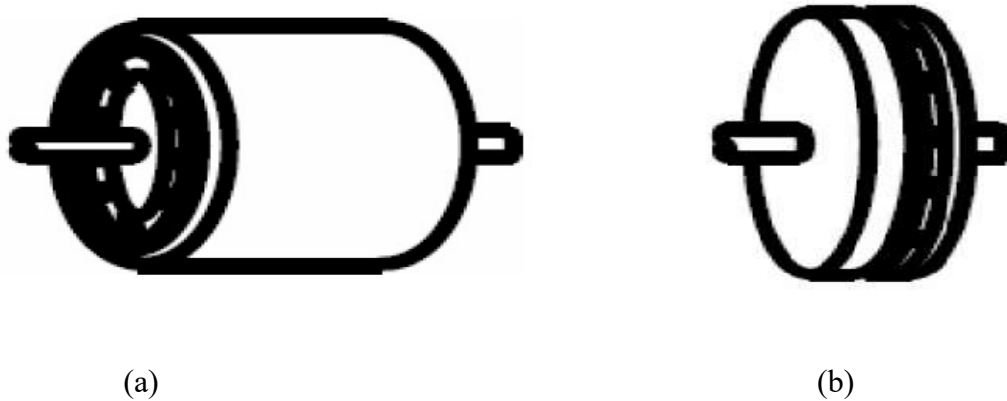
Vue schématique des machines: (a) à flux radial, (b) à flux axial
